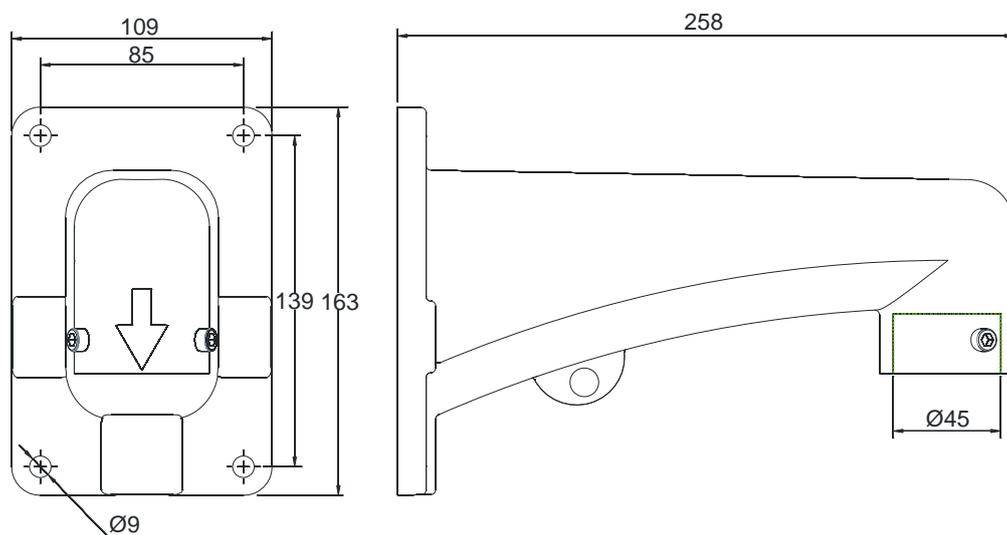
Immagine delle dimensioni del braccio di installazione a parete
